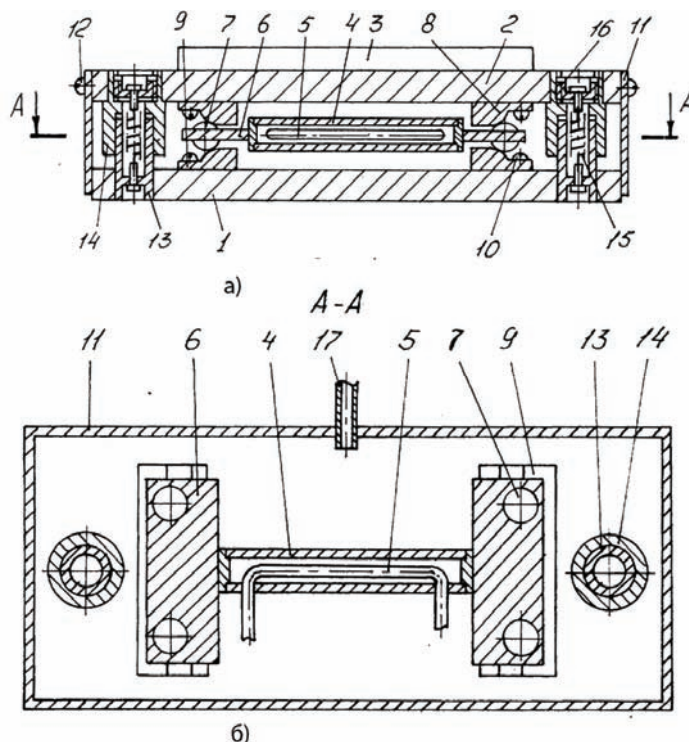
Устройство для микроподачи заготовок при шлифовании
